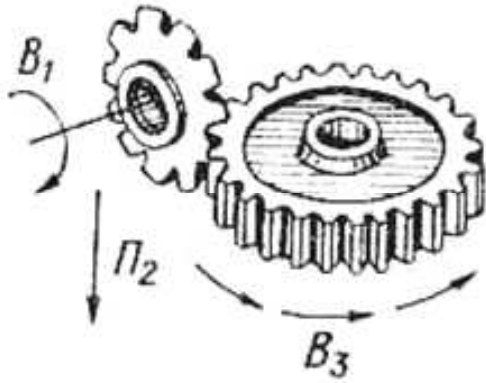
Схема способа зубофрезерования модульной (фасонной) фрезой
